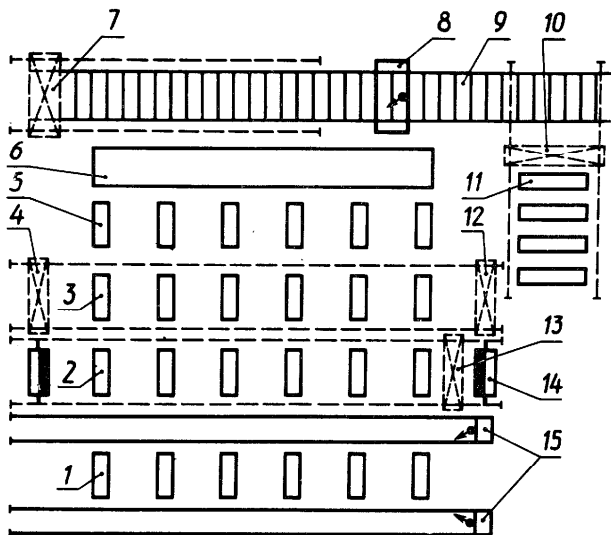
Схема поточной линии изготовления балок коробчатого сечения
